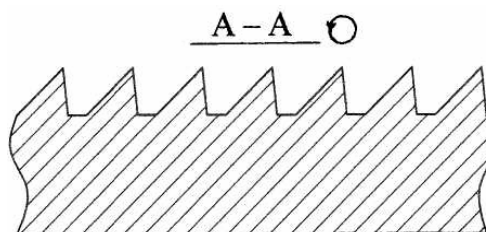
Продольный разрез внутренней боковой поверхности рабочей камеры
